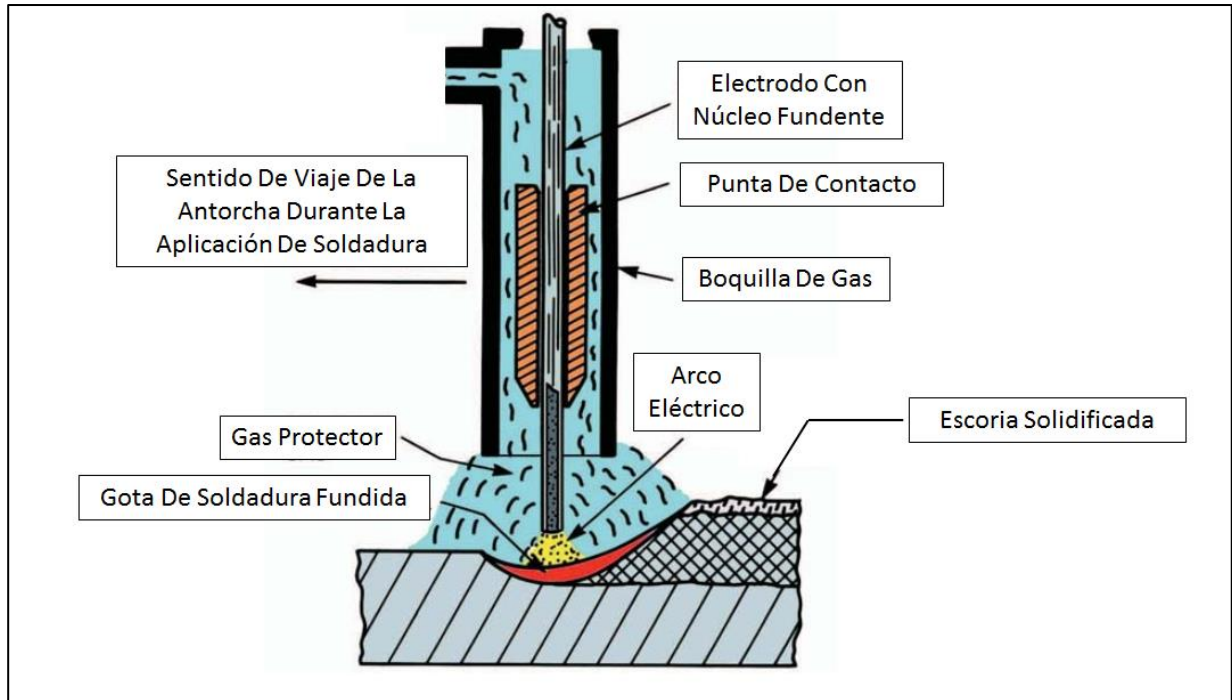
Proceso De Soldadura FCAW Con Protección Gaseosa [10].
